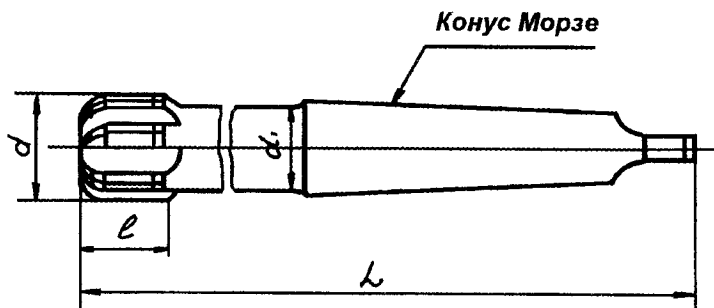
Насадна розвертка з твердосплавними пластинами
